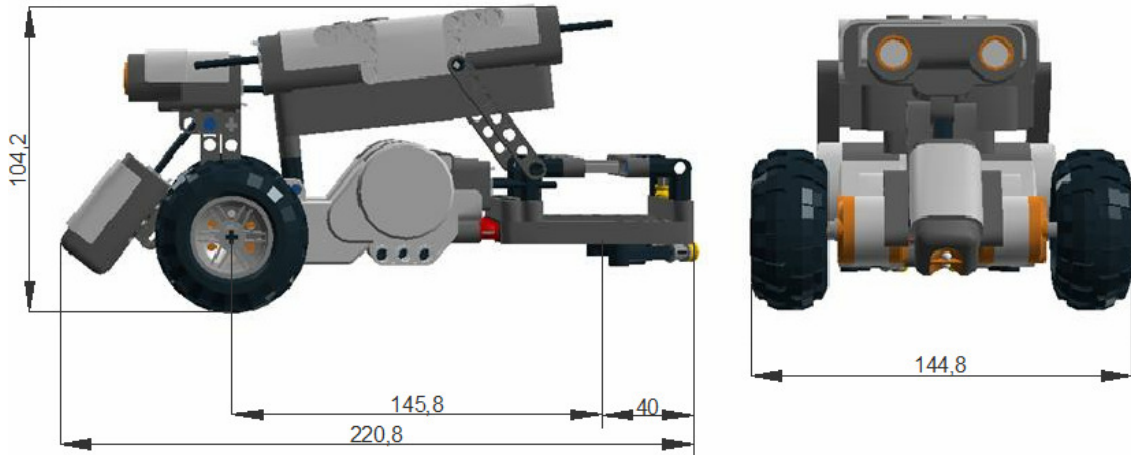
B3.): Dimensiones del tercer montaje.
